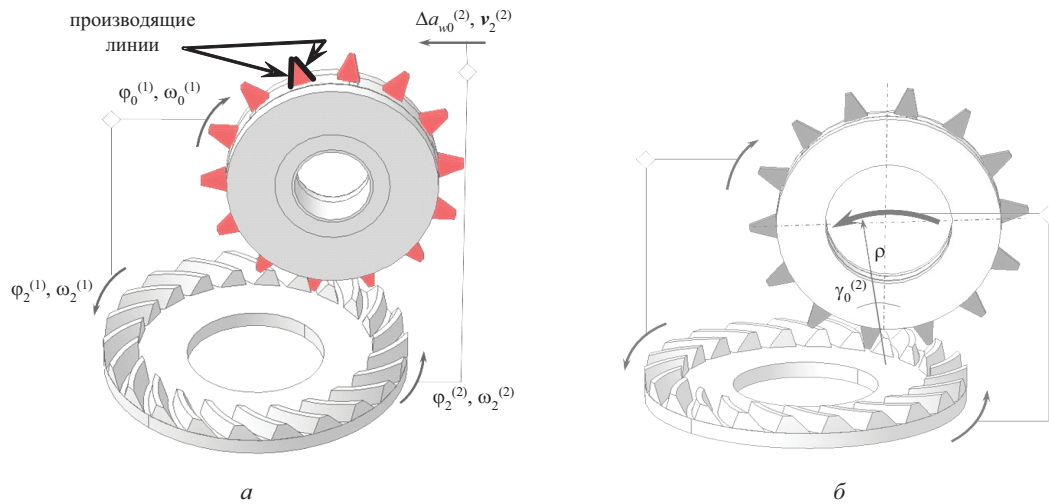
Формообразование зубьев спирального колеса производящей линией – режущей кромкой резца резцовой головки:
